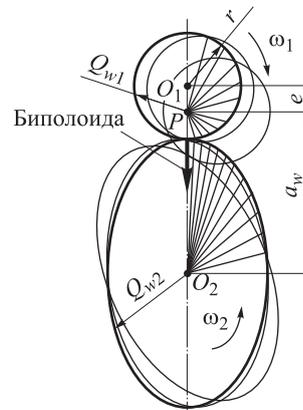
Схема центроид некруглых зубчатых колес для механизма G02
